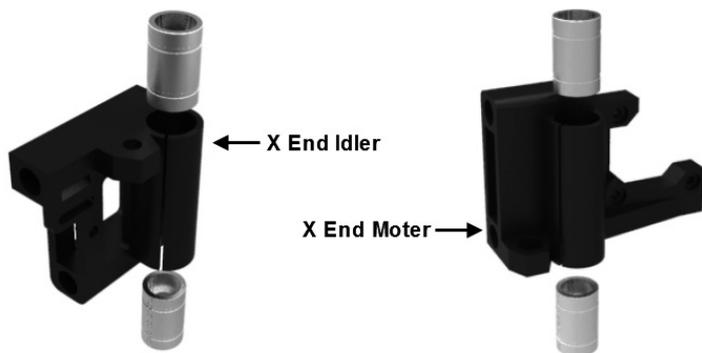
在 X End Idler 和 X End Motor 中安装 LM8UU
